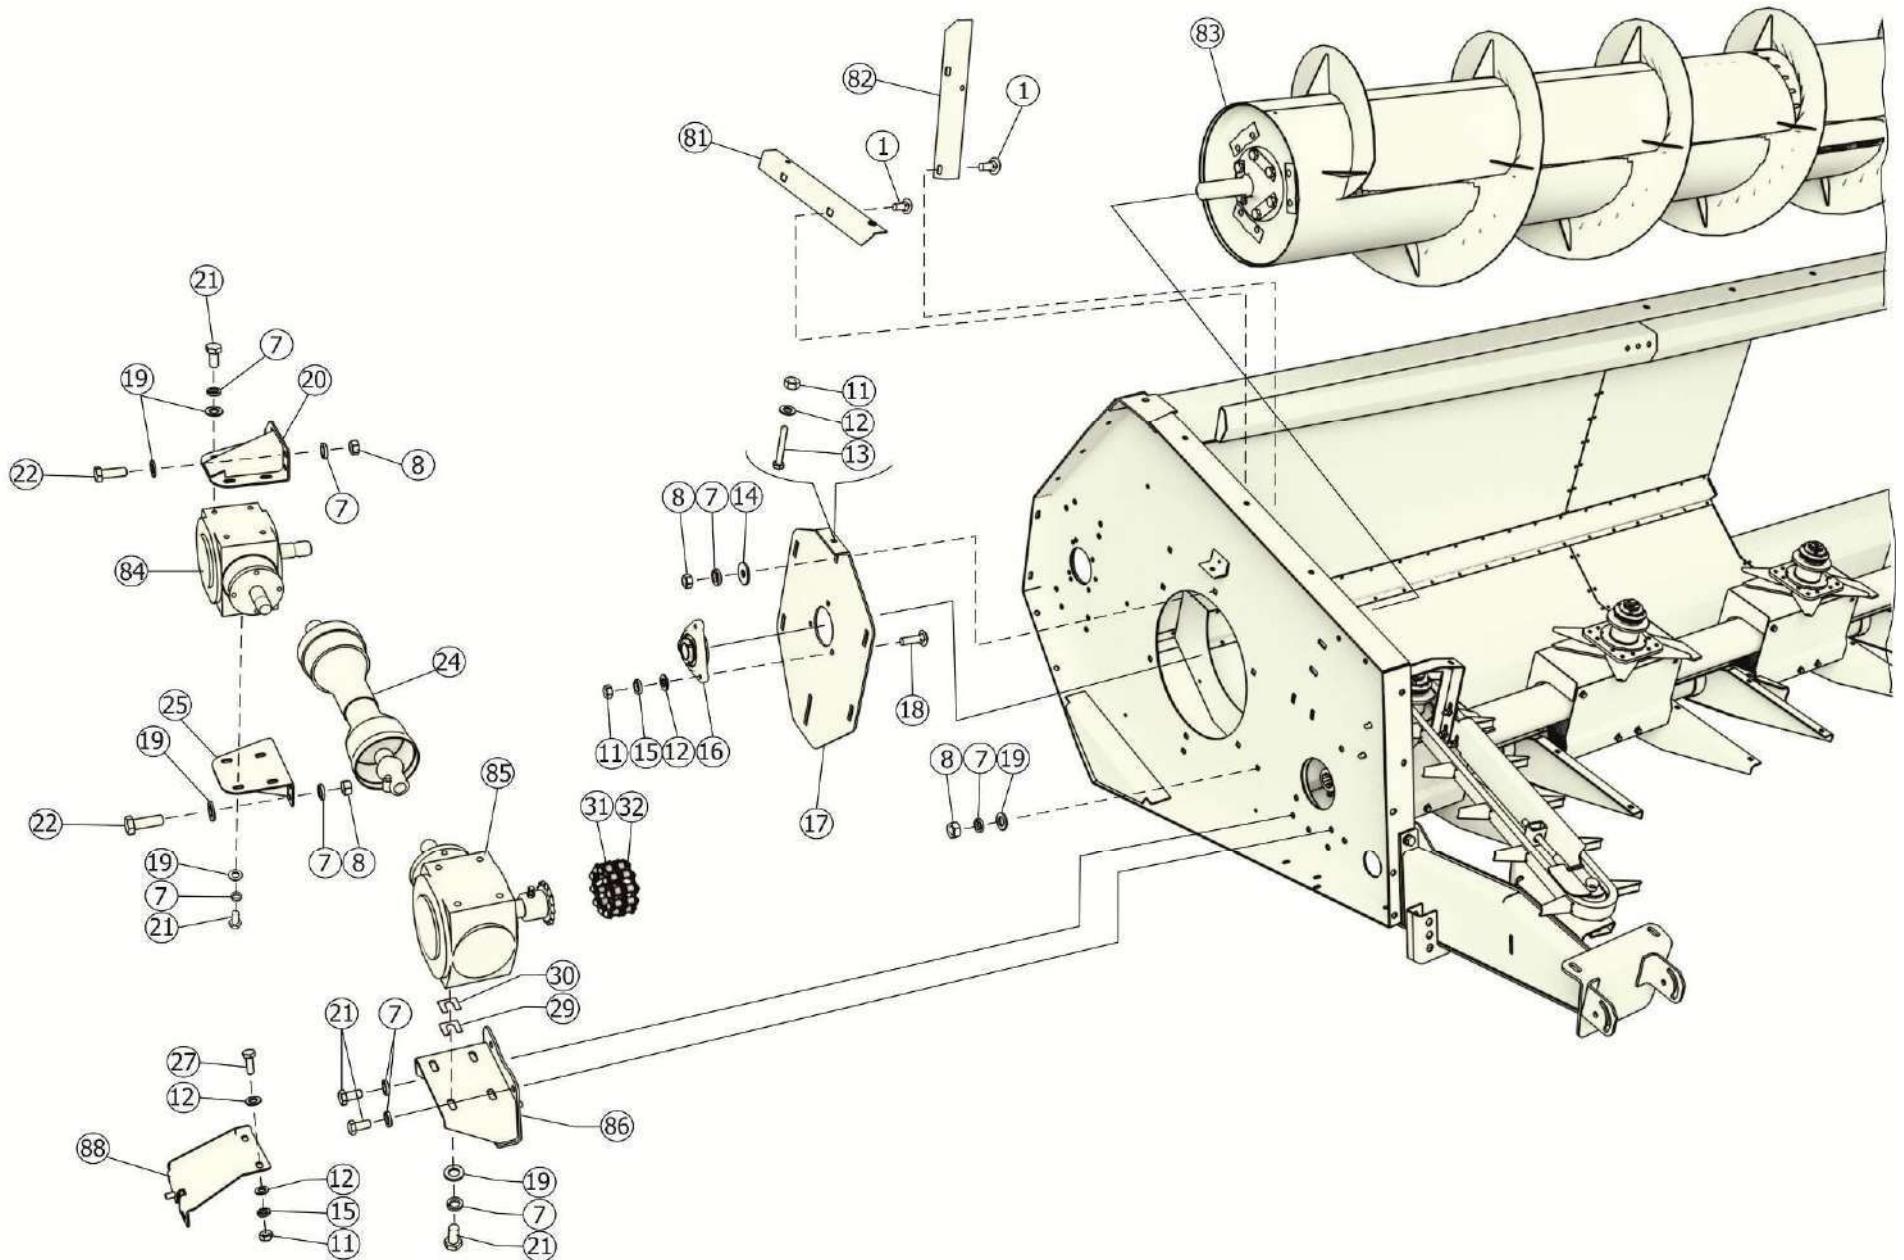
Корпус ПСП-810.01.01.000А. Вид справа
